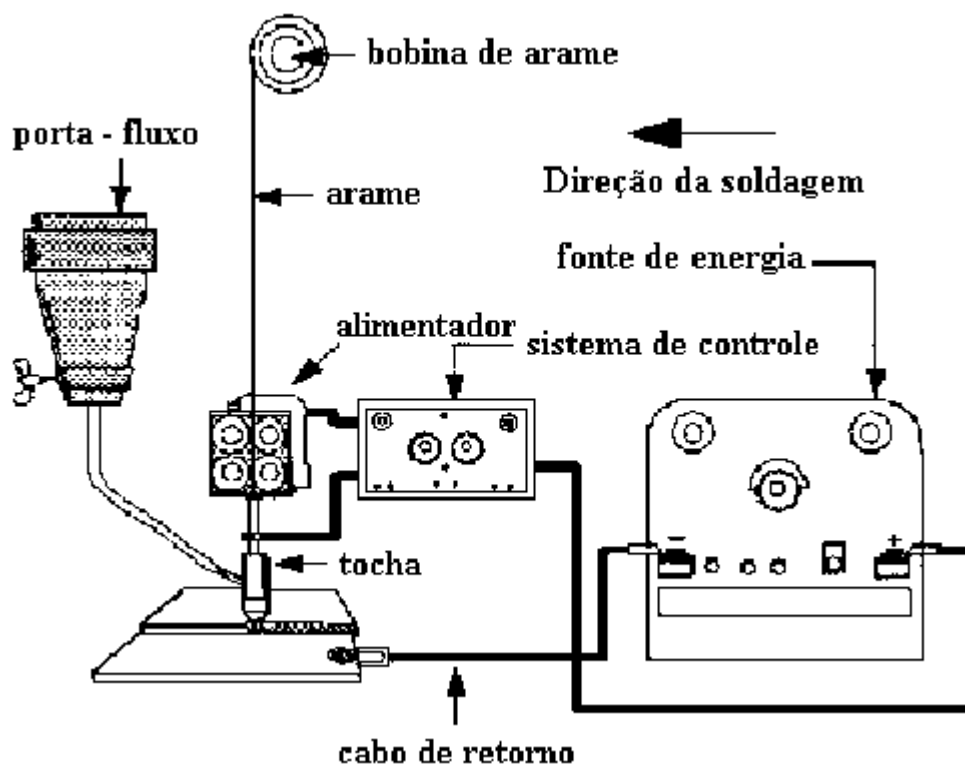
Equipamento básico para a soldagem a arco submerso. Fonte: Infosolda (2001)
